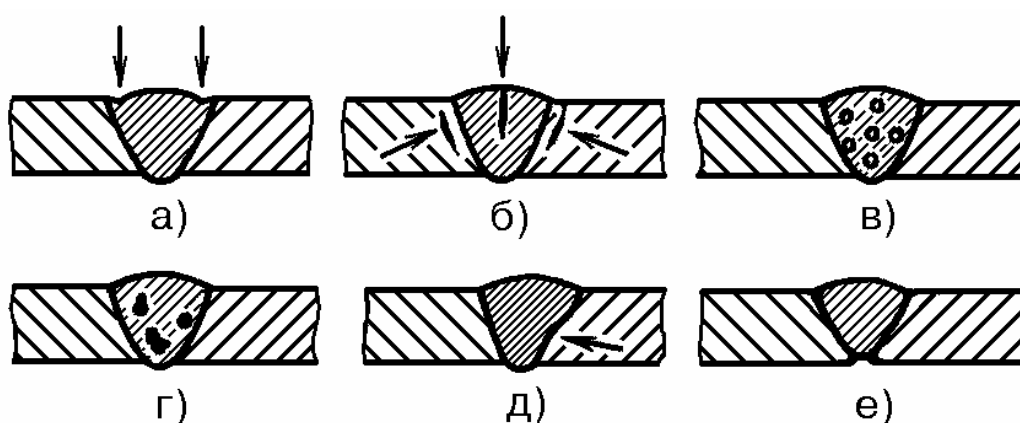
Поперечные сечения сварочных швов с типичными дефектами:
